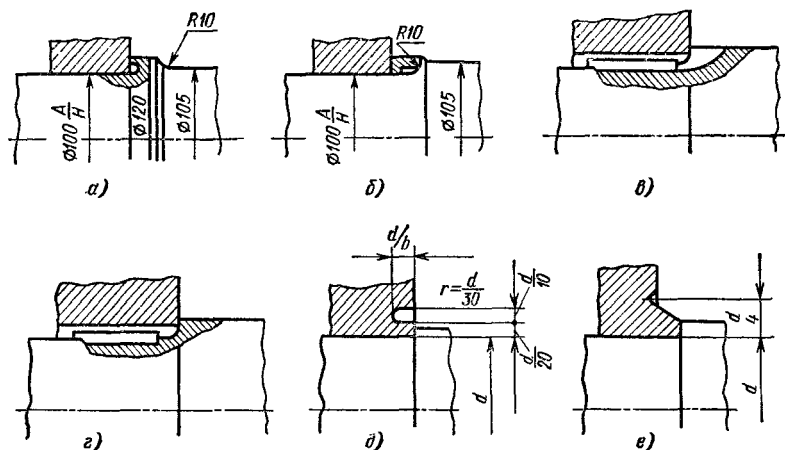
Различные способы конструктивного упрочнения вала с насаженной на него деталью
